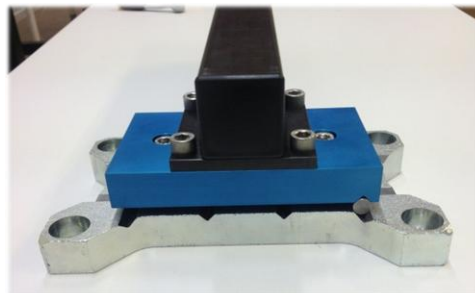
V-Cut monterad med Pick-up, bakifrån
